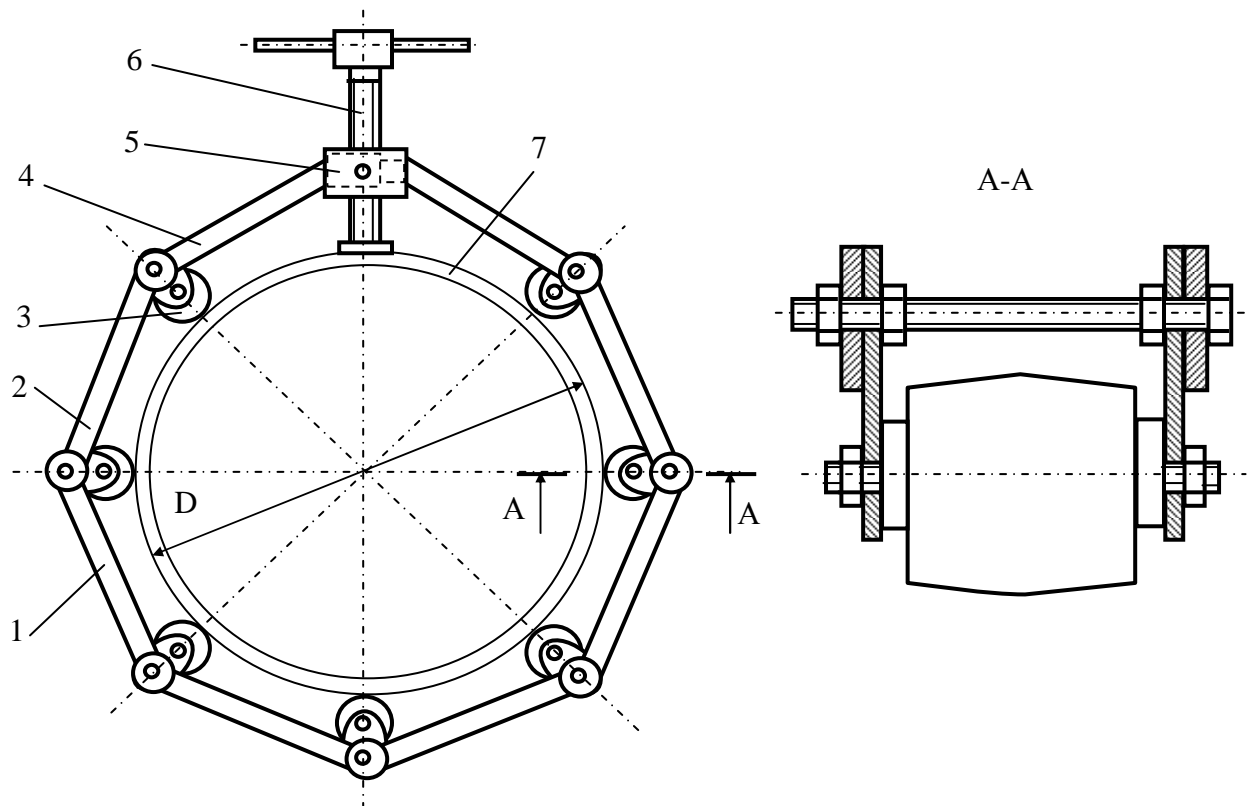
Зовнішній центратор для труб: 1-зовнішня ланка; 2-внутрішня ланка; 3-ролик; 4- гачок; 5-хрестовина; 6- гвинт; 7-труба.
